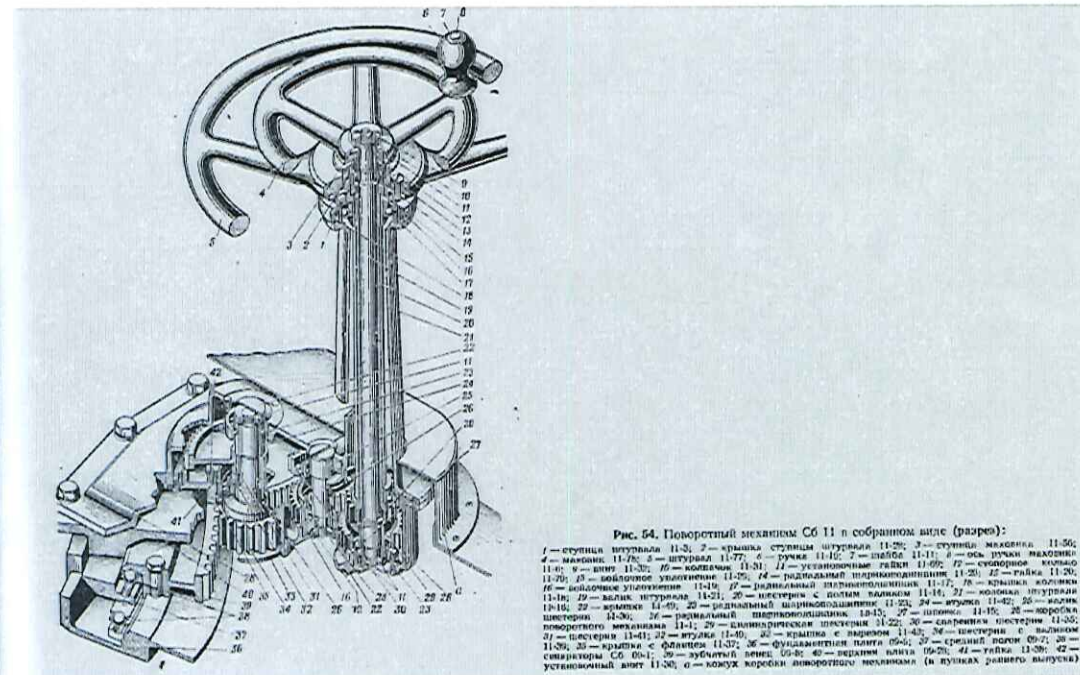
Поворотный механизм Сб 11 в собранном виде (разрез):
